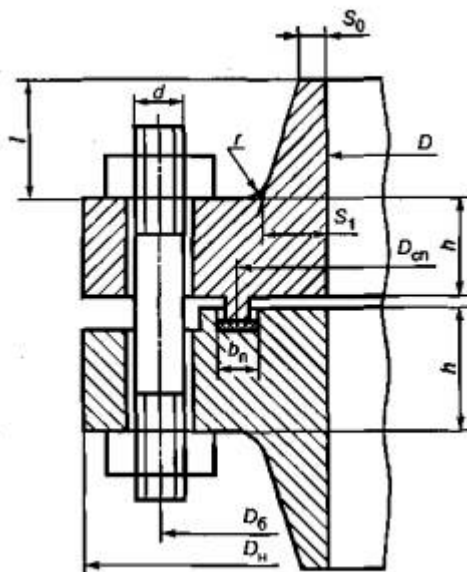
Фланцевое соединения с приварными встык фланцами с гладкой уплотнительной поверхностью типа шип – паз
